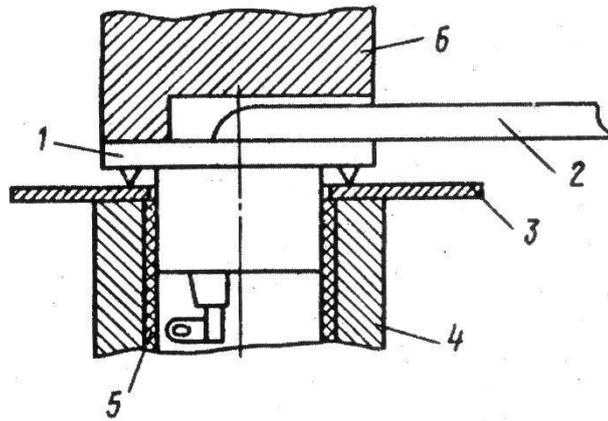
Схема рельефной сварки тэна с боковиной электрорадиатора:
